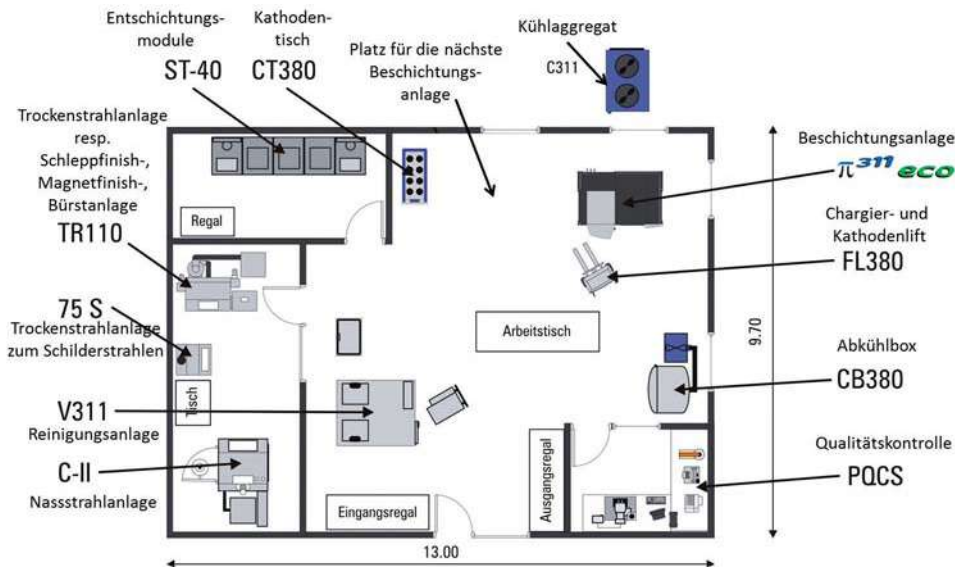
Beispiel-Layout eines In-House-Beschichtungssystems.
